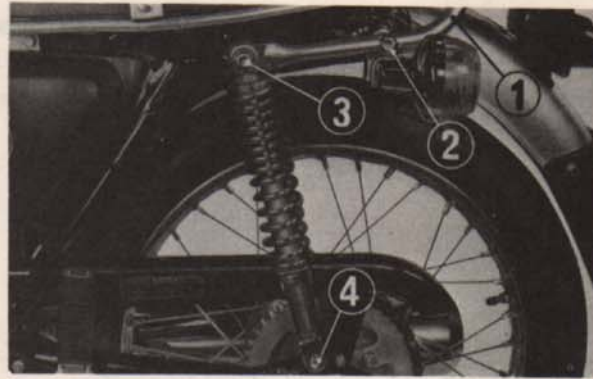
(1) Tube métallique de pare-chocs arrière
